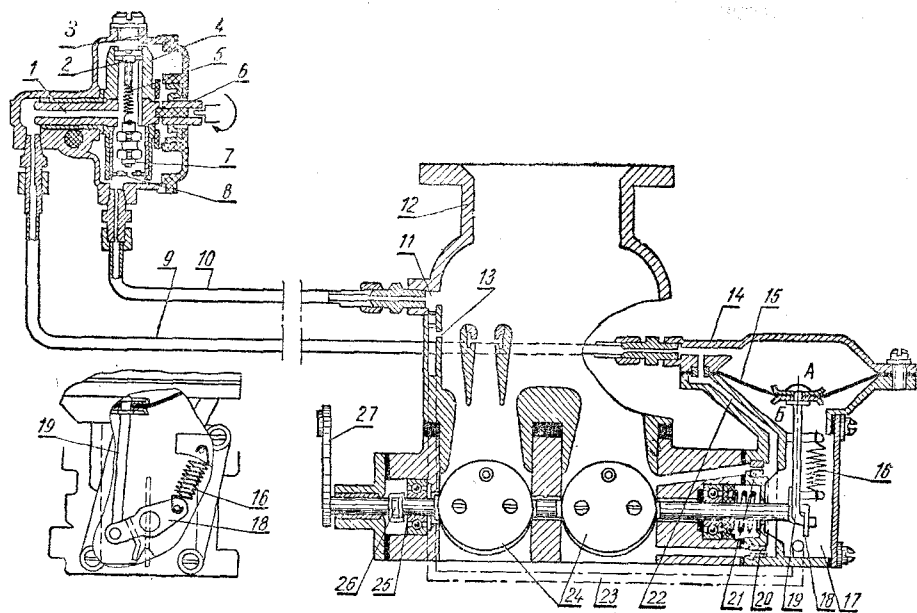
Схема пневмоцентробежного ограничителя максимального числа оборотов коленчатого вала двигателя:
